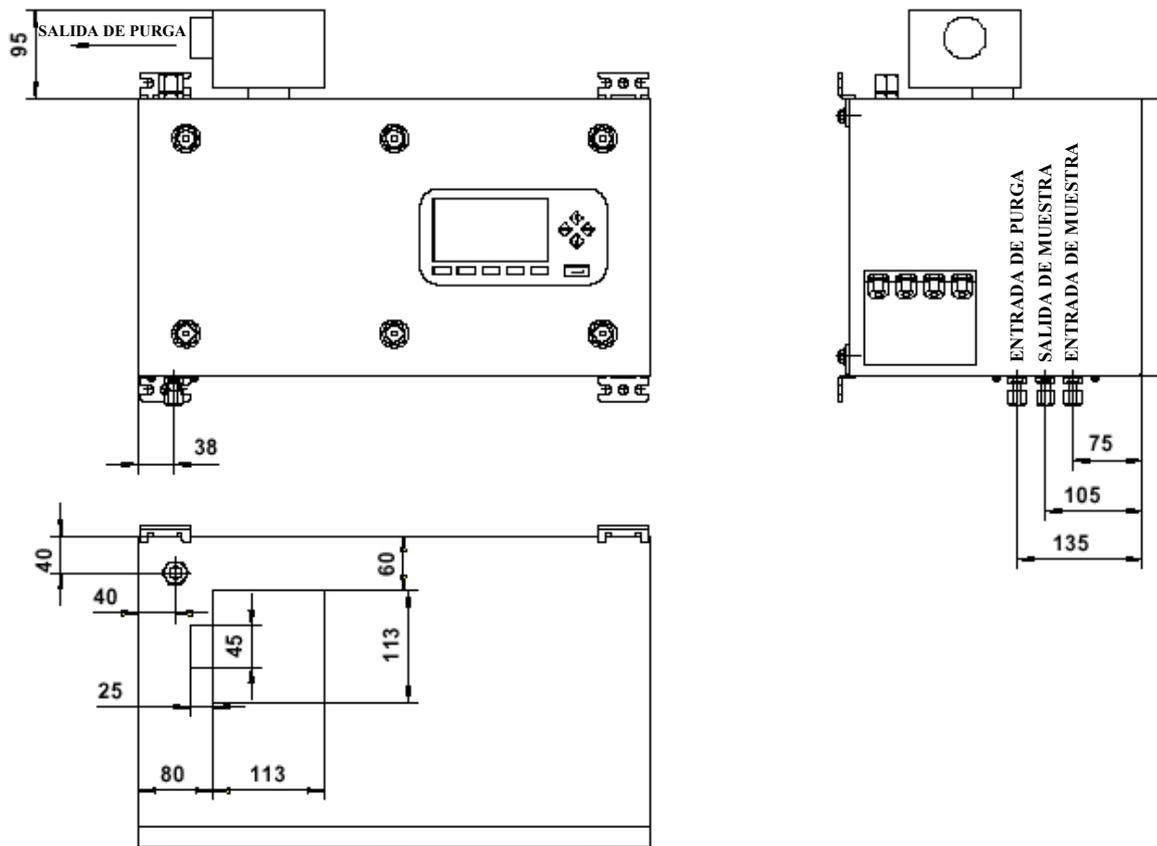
Croquis dimensional del MLT 2 para zona 2 Ex con carcasa estándar (todas las dimensiones figuran en mm).
